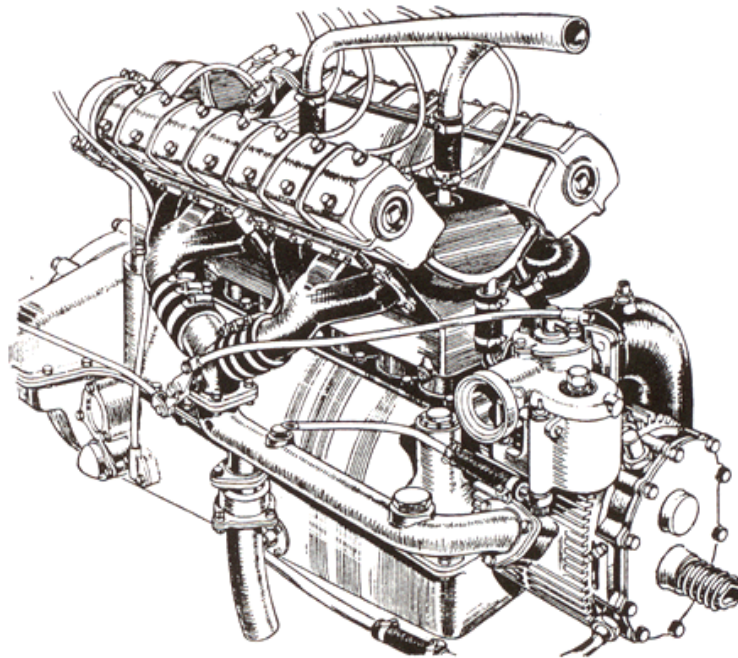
Motor de la marca inglesa SUNBEAM, de 1924, provisto de compresor volumétrico Roots.
